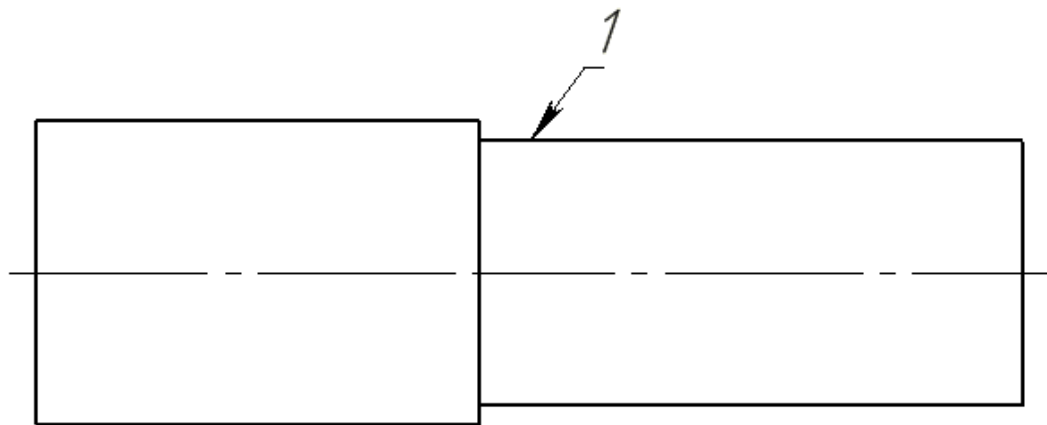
Обробка зовнішньої циліндричної поверхні 1
